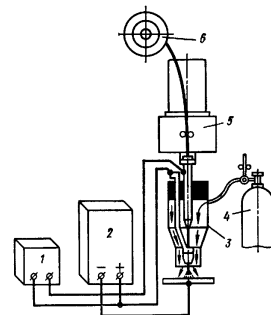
Схема газозлектрической сварки с предварительным подогревом электродной проволоки:
